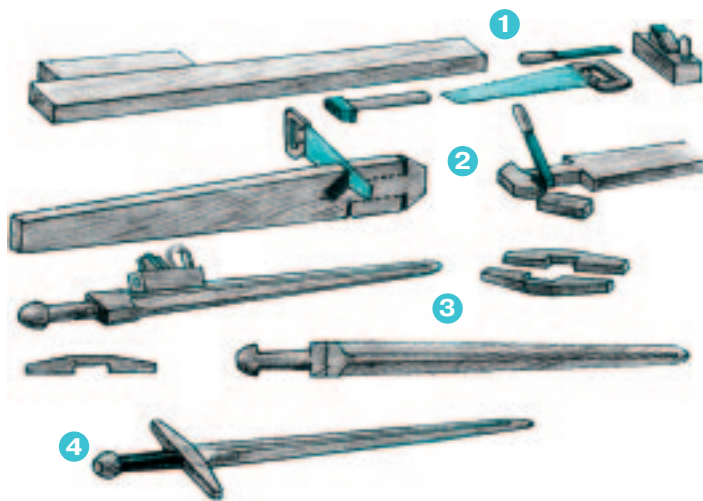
Порядок изготовления рыцарского меча: 1 — исходные материалы и инструменты; 2 — изготовление заготовки; 3 — детали меча; 4 — готовый меч.
